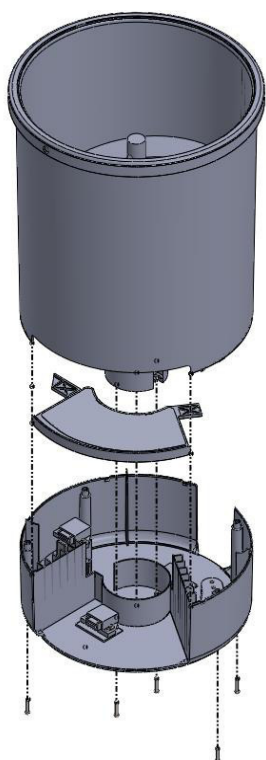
Montagem da parte superior e inferior do balde de compostagem, bem como da bampa da gaveta de saída de composto.
